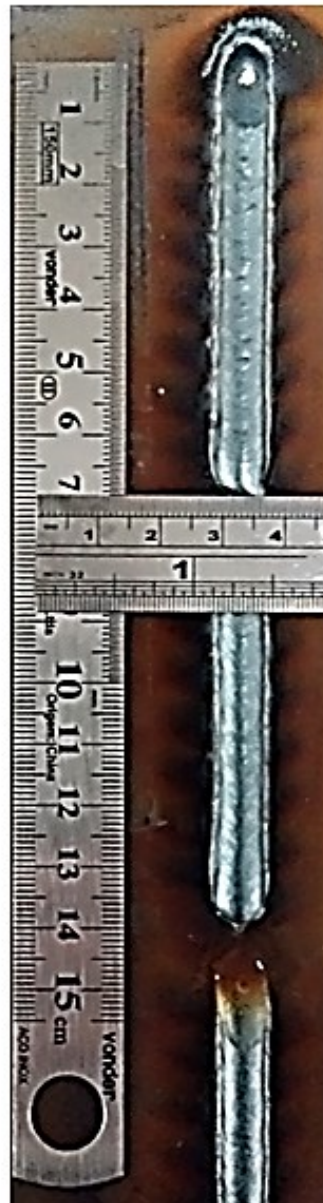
Soldagens GMAW pulsada. Com oscilação do arco Bx=2,8 mT
